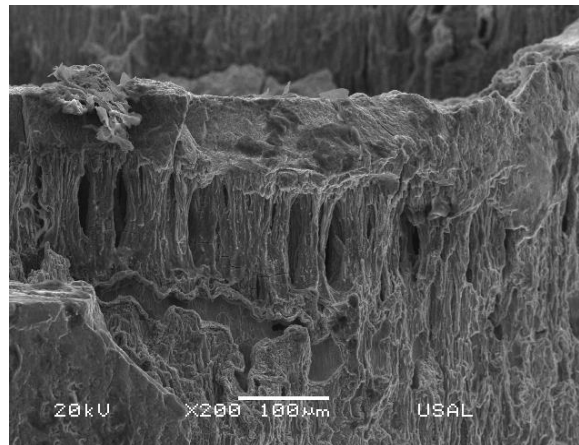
Fractografía de la zona exterior de la fisura del E7 ensayado a fractura en DAL.
